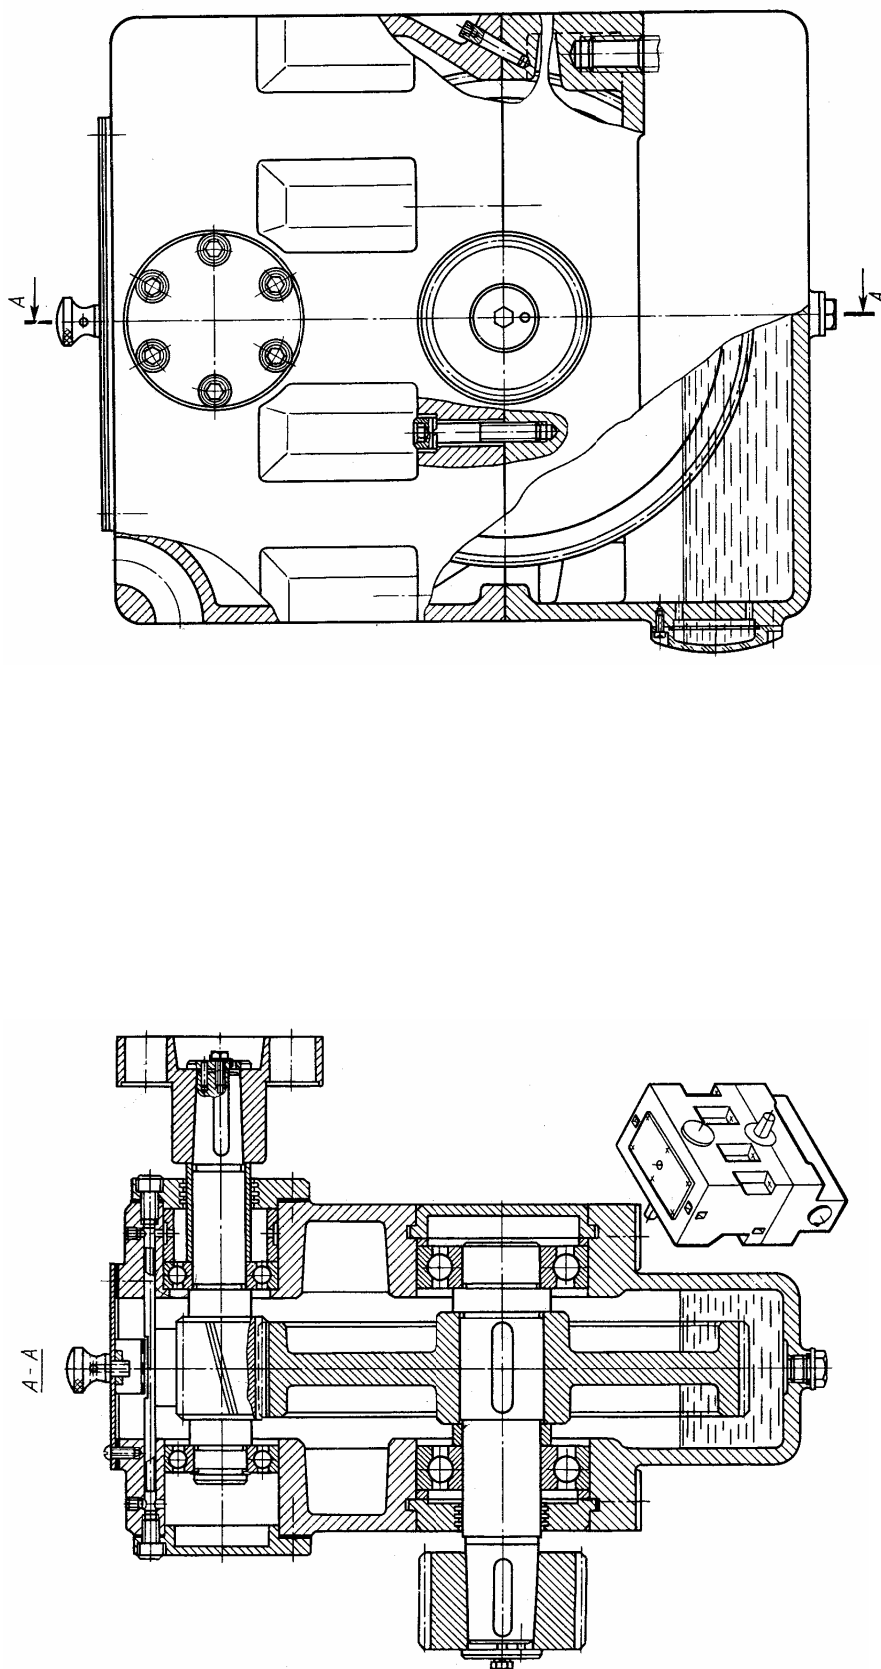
Редуктор (А3) цилиндрический одноступенчатый вертикальный с верхним расположением шестерни
